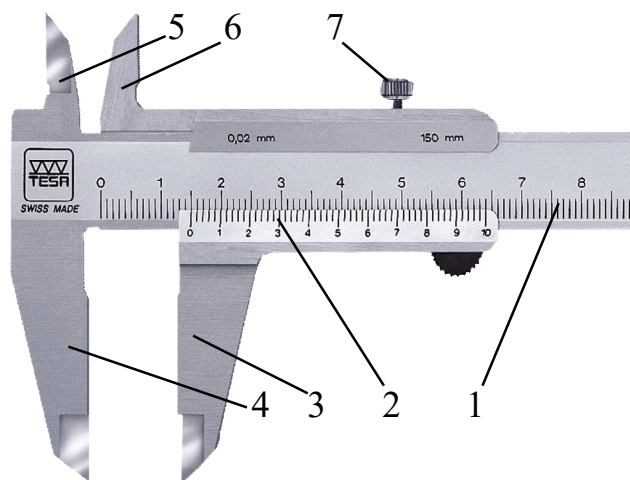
Штангенциркуль: 1 – штанга; 2 – ноніус; 3, 4 – нижні губки; 5, 6 – верхні губки; 7 – гвинт
